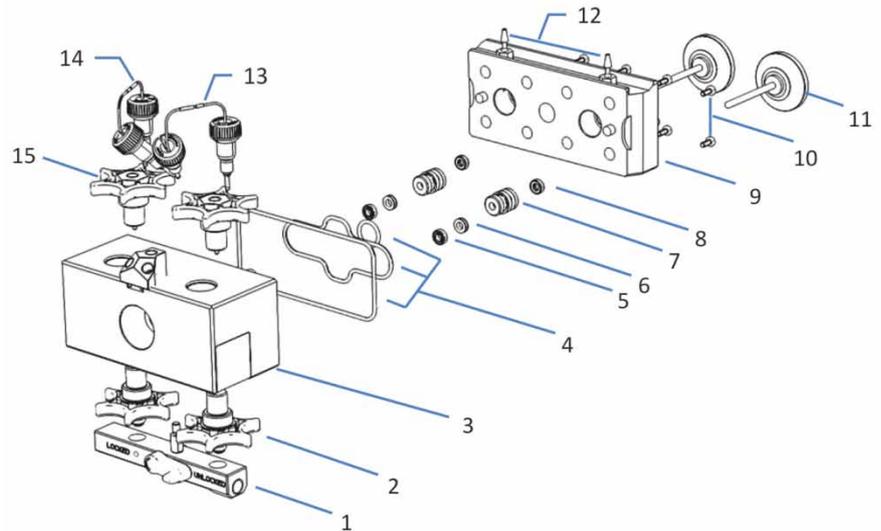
Vue d'ensemble des éléments de tête de pompe
